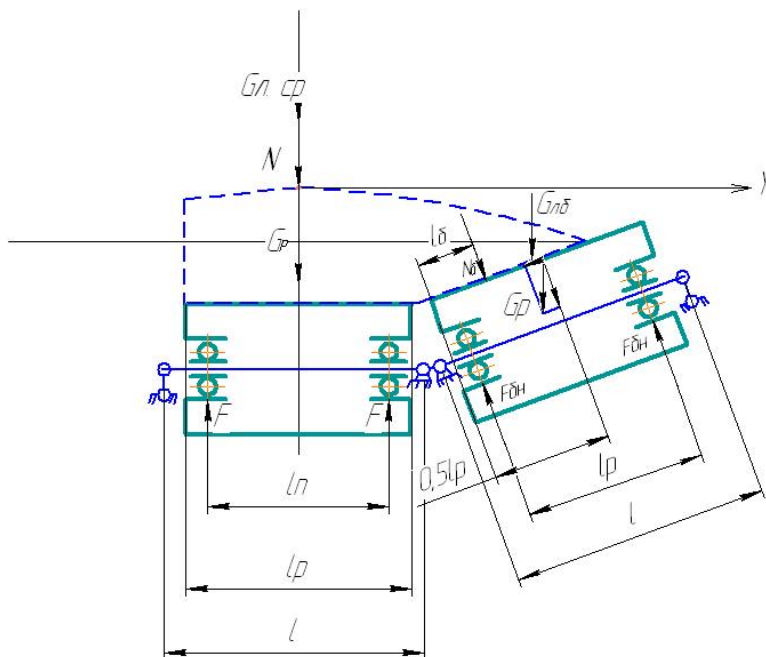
Расчетная схема для определения радиальных нагрузок на подшипники трехроlikовой опоры
